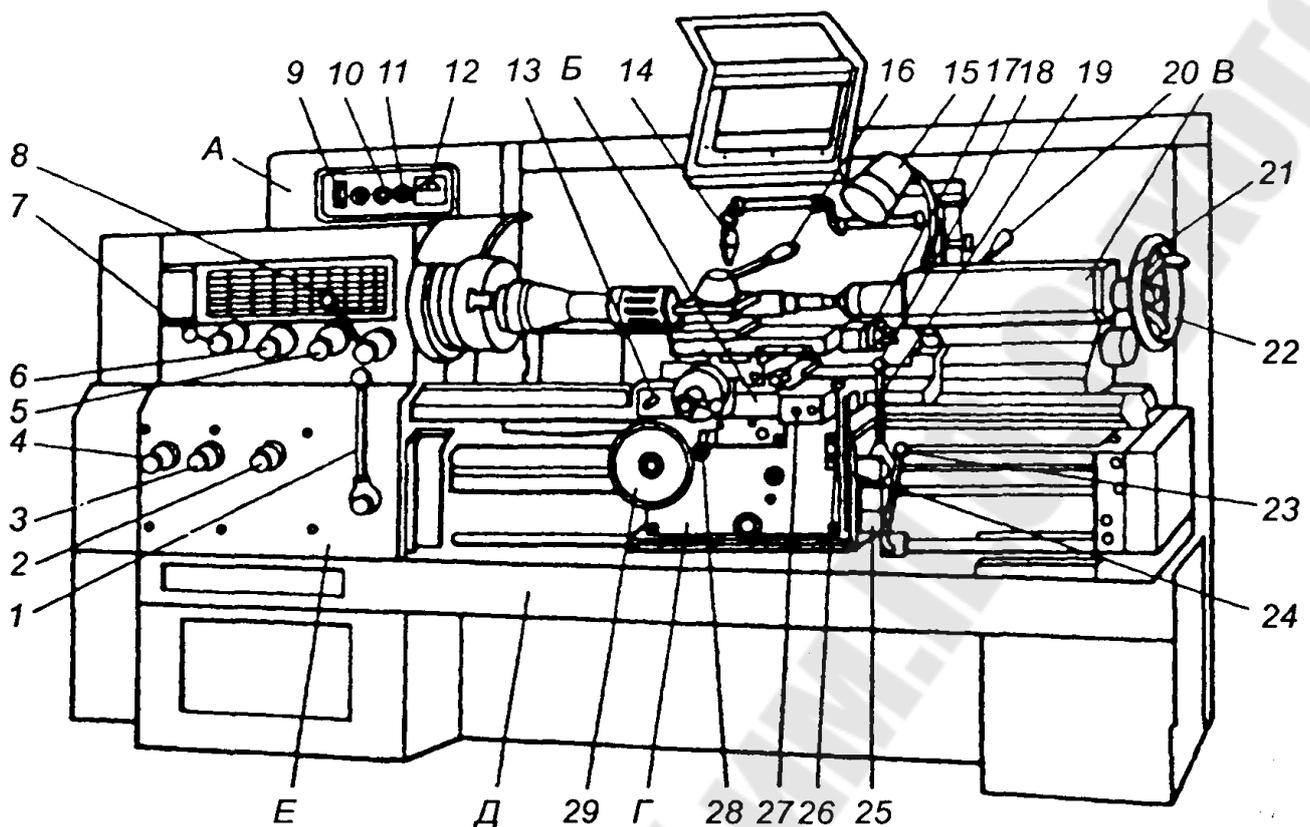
Общий вид токарно-винторезного станка: А — передняя бабка; Б — суппорт; В — задняя бабка; Г — фартук; Д — станина; Е — коробка подач; 1 — рукоятка управления фрикционной муфтой главного привода; 2 — вариатор подачи, шага резьбы и механизма отключения подачи; 3 — вариатор подачи и типа нарезаемой резьбы; 4 — вариатор подачи и шага резьбы; 5 — переключатель на левую, правую и другие резьбы; 6 — рукоятка установки нормального и увеличенного шага резьбы и положение при делении на ходы резьбы; 7, 8 — рукоятки установки частоты вращения шпинделя; 9 — вводный автоматический выключатель; 10 — лампа сигнальная; 11 — включение насоса СОЖ; 12 — указатель нагрузки станка; 13 — ручное перемещение поперечных салазок суппорта; 14 — регулируемое сопло СОЖ; 15 — освещение местное; 16 — рукоятка поворота и зажима резцедержателя; 17 — рукоятка перемещения верхних салазок суппорта; 18 — рукоятка включения двигателя ускоренного хода; 19 — рукоятка управления перемещения каретки и салазок суппорта; 20 — зажим пиноли задней бабки; 21 — рукоятка закрепления задней бабки на станине; 22 — маховик перемещения пиноли задней бабки; 23, 24 — рукоятки включения и отключения муфты главного привода; 25 — включение подачи; 26 — винт закрепления каретки на станине; 27 — кнопочная станция двигателя главного привода; 28 — рукоятка включения и выключения ременной шестерни; 29 — маховик ручного перемещения
